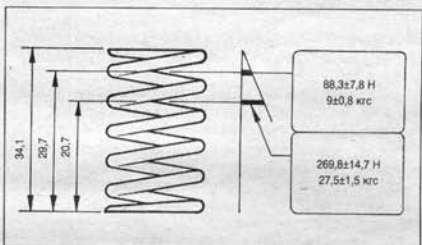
Основные данные для проверки внутренней пружины клапана
